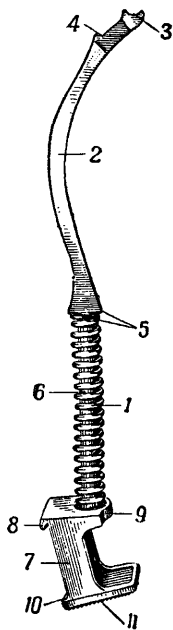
Боевая пружина с толкателем и защелкой магазина:
